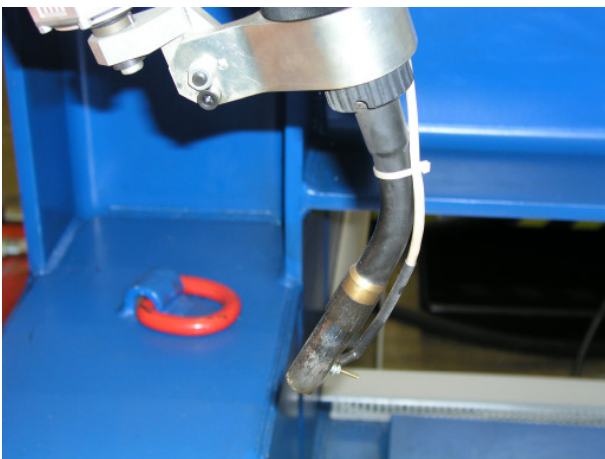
Anschluss des Spannungssensors an den Schweißbrenner
